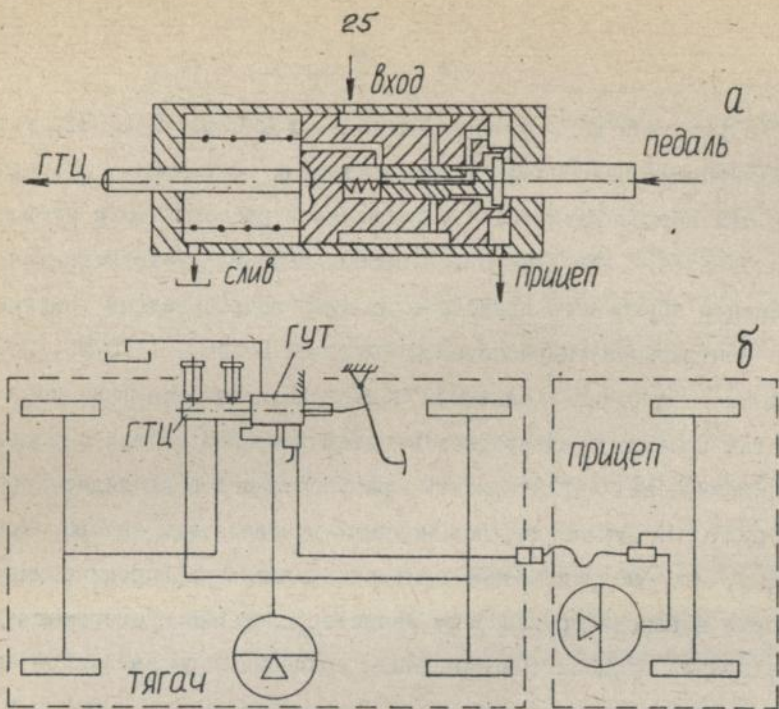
Комбинированный гидросиловой привод: а-ГУТ типа закрытый центр, б-концепция привода
